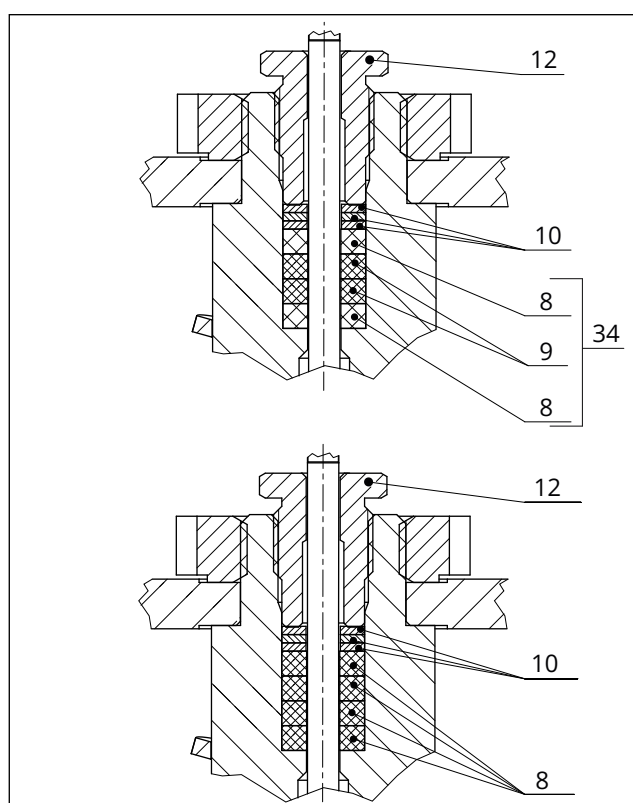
Garnitures de presse-étoupe ajustables : joints composite PTFE et PTFE blanc (en haut) · Joints PTFE blanc (en bas)
